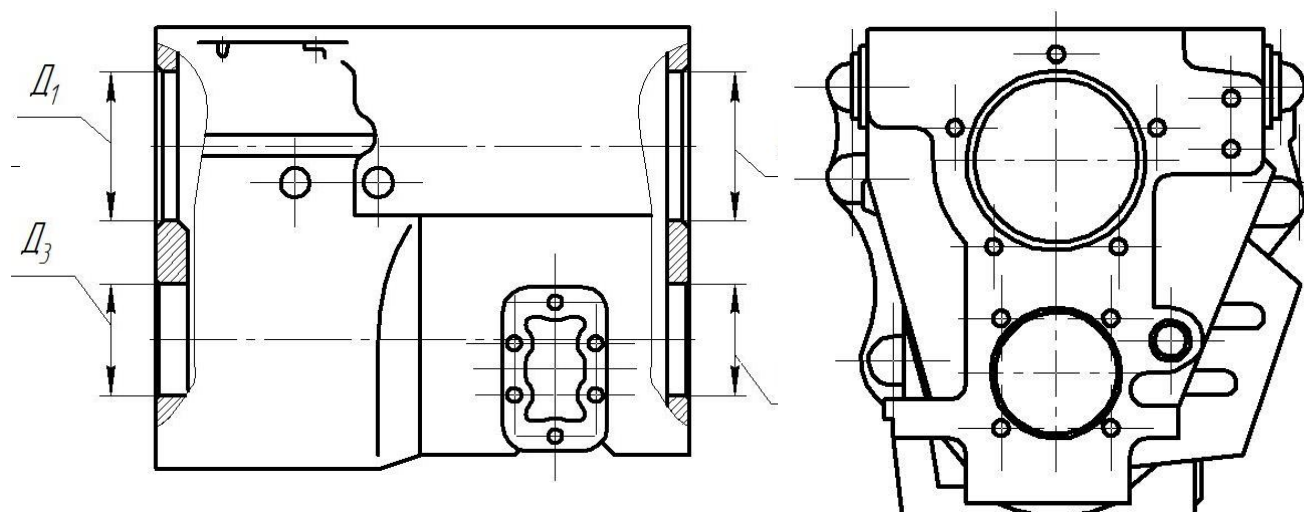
Картер коробки передач (раздаточной или КОМ)
